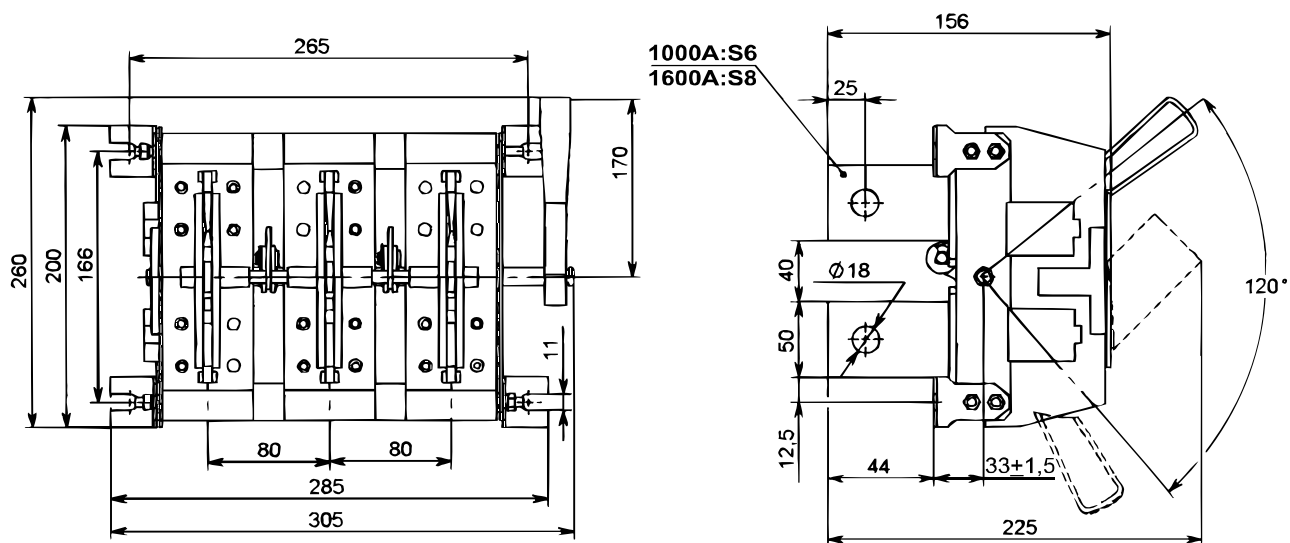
Разъединитель РЕ19-41(43)-32220-00 УХЛЗ с боковой рукояткой, заднего присоединения шин
